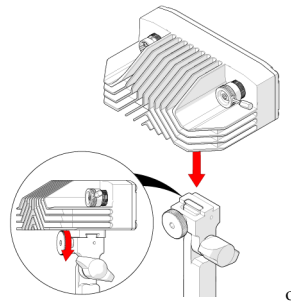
Fixer la caméra et serrer la vis à ailettes
